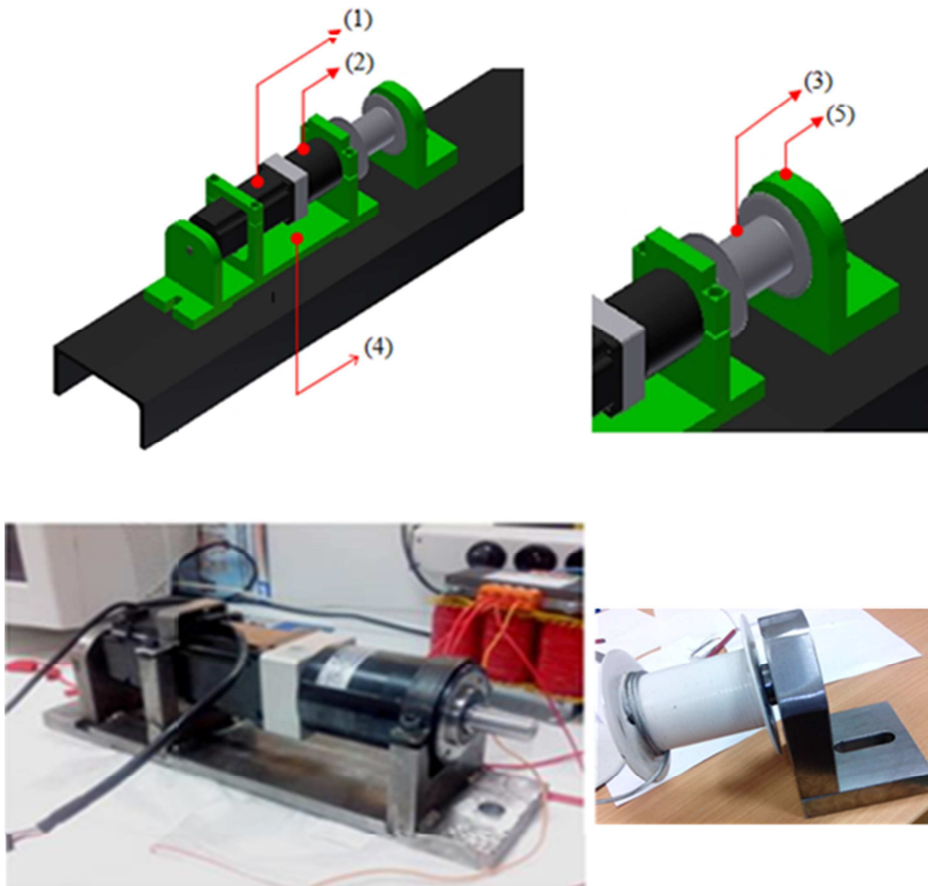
Vue d'ensemble de la motorisation actuelle.
